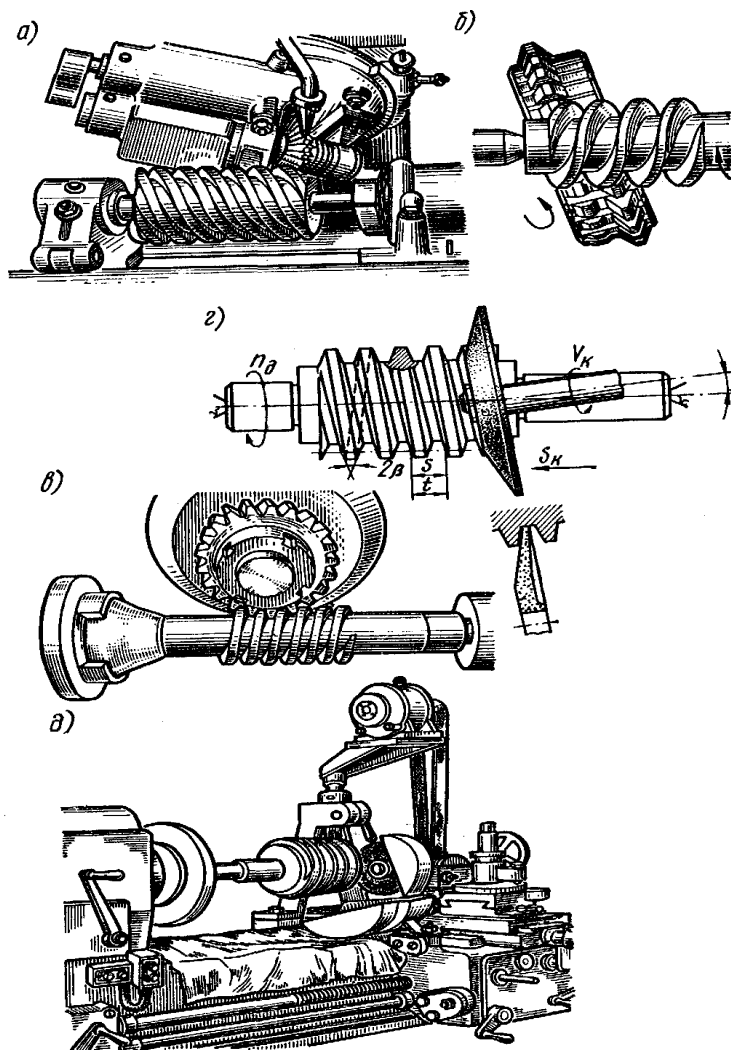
Обработка червяков: а – дисковой фрезой; б – фрезой-улиткой; в – долбяком; г – шлифовальным кругом; б – специальное устройство для шлифования червяка на токарном станке
